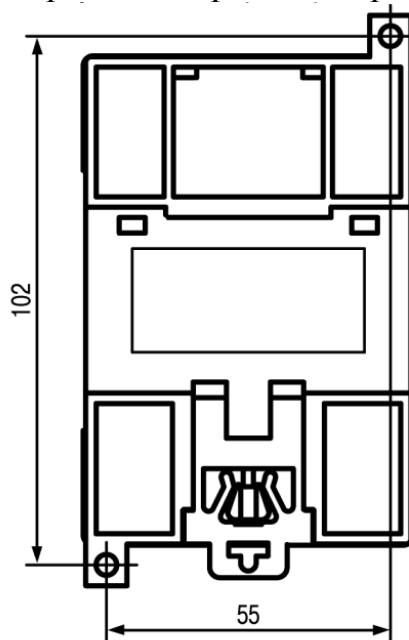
Габаритный чертеж модуля МУ110-16Р
